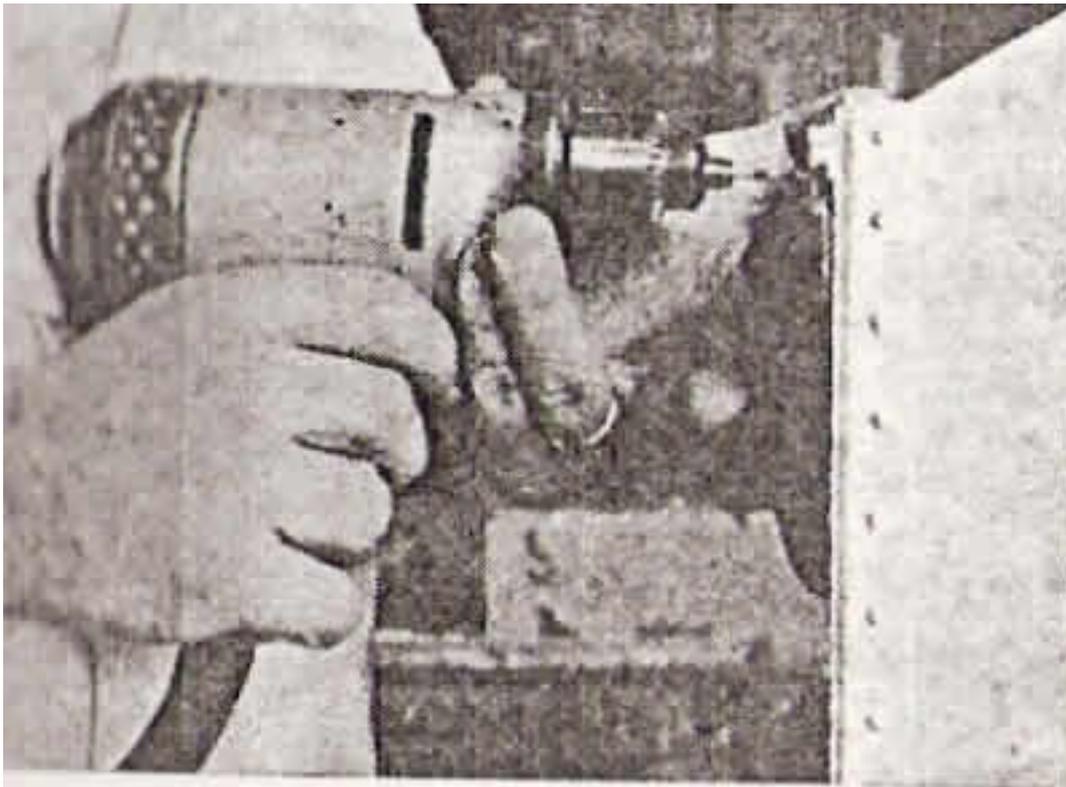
Forma de sostener una taladradora portátil para iniciar un taladro
